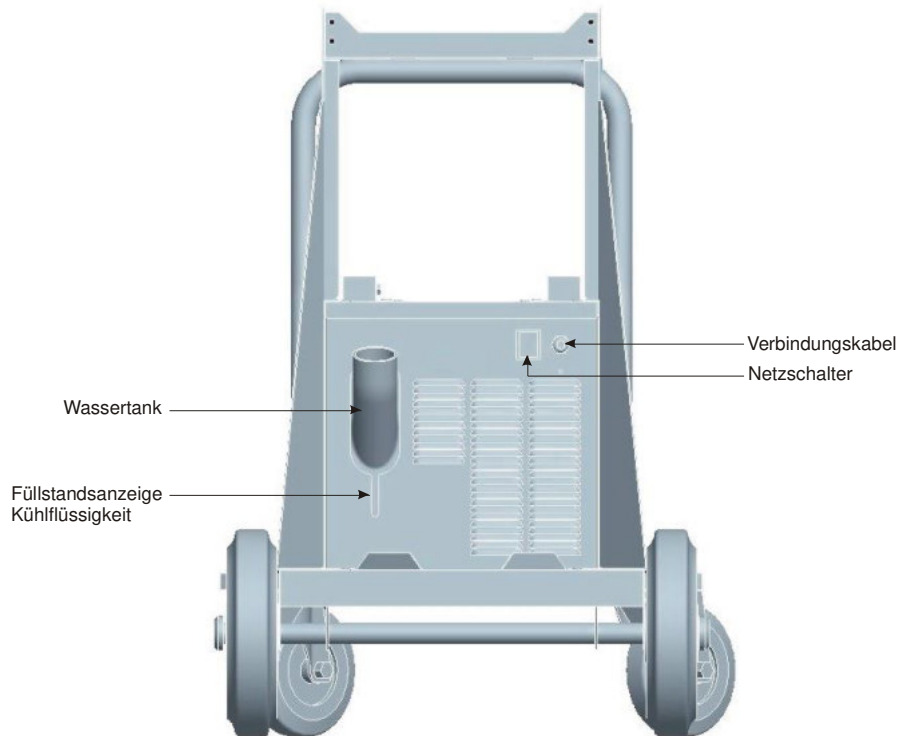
MIG - COOL CART 100 Ansicht von Hinten
